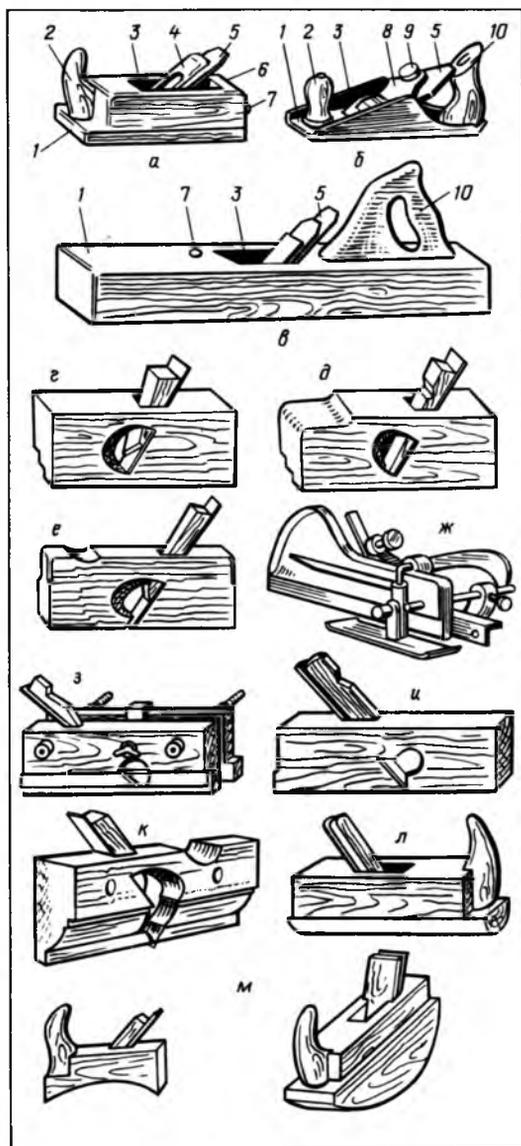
Строгальный инструмент: а — деревянный рубанок; б — металлический рубанок; в — фуганок (1 — корпус; 2 — державка; 3 — леток; 4 — клин; 5 — нож; 6 — упор; 7 — пробка; 8 — прижим; 9 — винт; 10 — ручка); г — отборник; д — фальцгебель; е — зензубель; ж — шпунтубель; з — грунтобель; и — штап; к — калевка; л — галтель; м — горбачи (с вогнутым и выпуклым дном)
